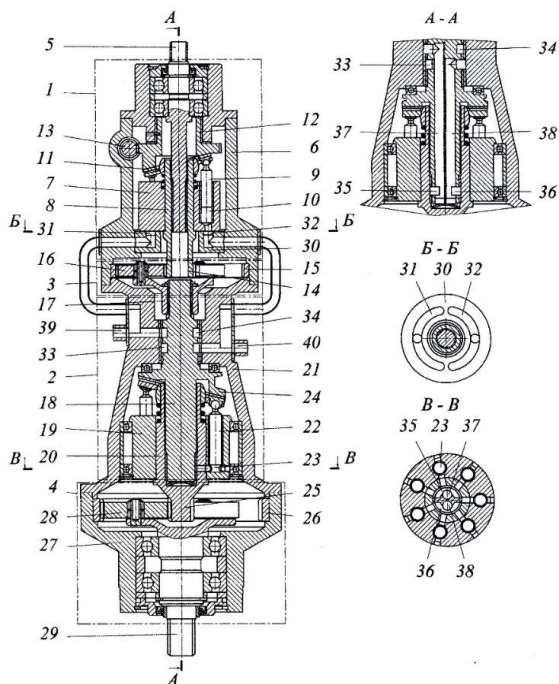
Конструктивная схема ОГП с внутренним разветвлением потока мощности
